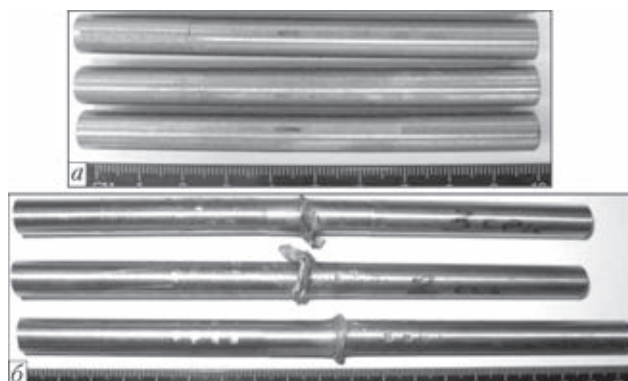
Заготовки, полученные на основе метода порошковой металлургии: а — прессованные; б — сваренные (прутки)
